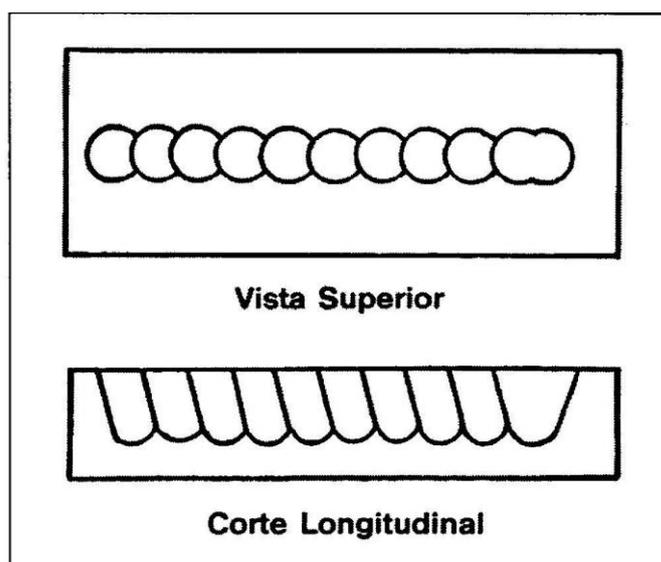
Soldadura obtenida por el proceso TIG.
